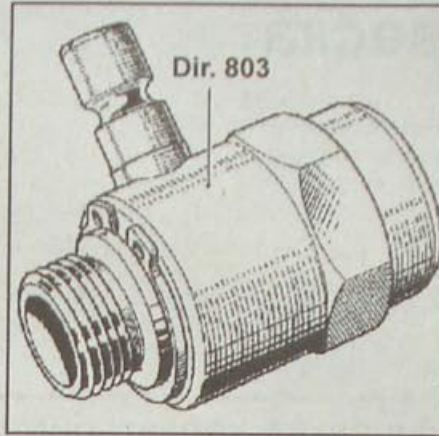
Переходник Dir. 803 с метрической резьбой
